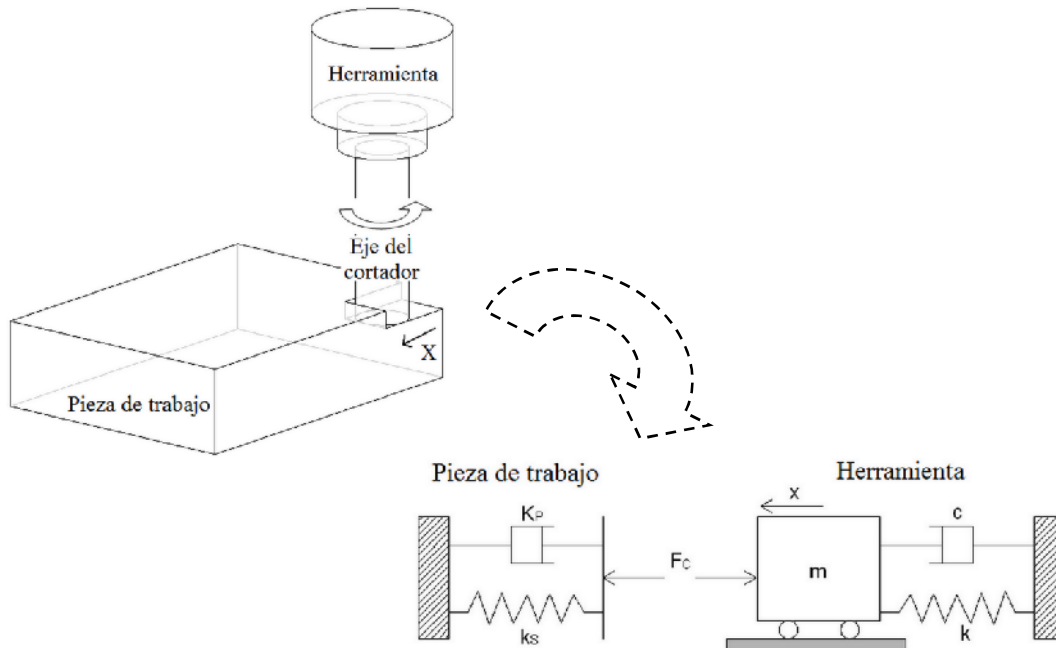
Modelo de una herramienta y una pieza de trabajo durante el fresado (Adaptado de [106]).
